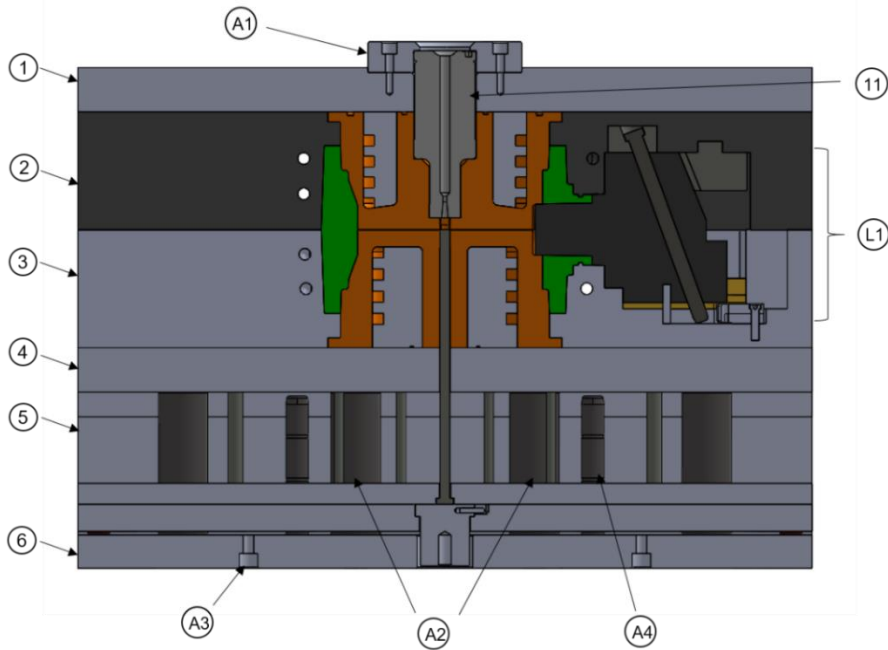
Vista Sección Molde Mecánico, Molde Cerrado
